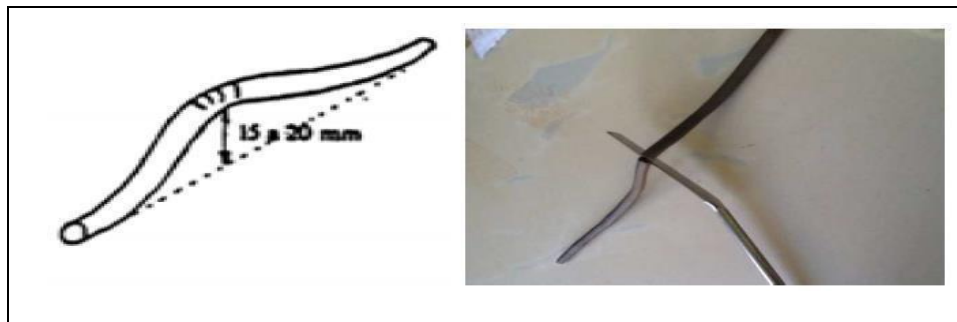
La fissuration et brisure du rouleau (Cheheb. F ,2016).
